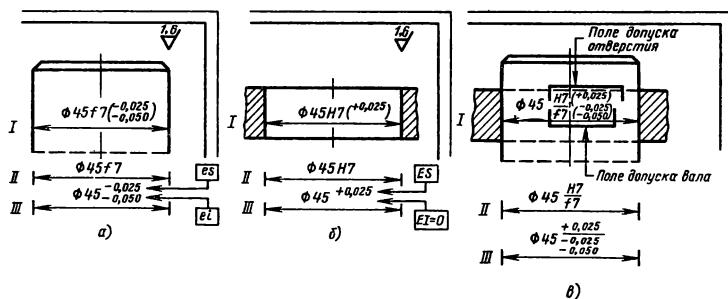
Варианты (I, II, III) обозначения полей допусков на чертежах:
